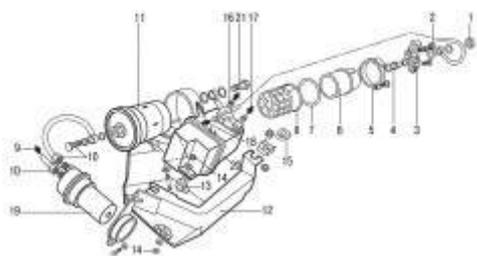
Топливный бак и топливный насос автомобилей с двигателем ООСН: 1 – гайка; 2 – пробка; 3 – переходник; 4 – клапан; 5 – кольцо крепления; 6 – топливный насос; 7 – уплотнение; 8 – фильтр; 9 – топливопровод к распределителю; 10 – соединительная муфта; 11 – топливный фильтр; 12 – кронштейн; 13 – резиновый демпфер; 14 – гайка; 15 – пружинная скоба; 16 – возвратная трубка; 17 – штуцер трубопровода от всасывающего насоса; 18 – штуцер трубопровода возврата топлива; 19 – аккумулятор давления; 20 – бачок насоса; 21 – болт
